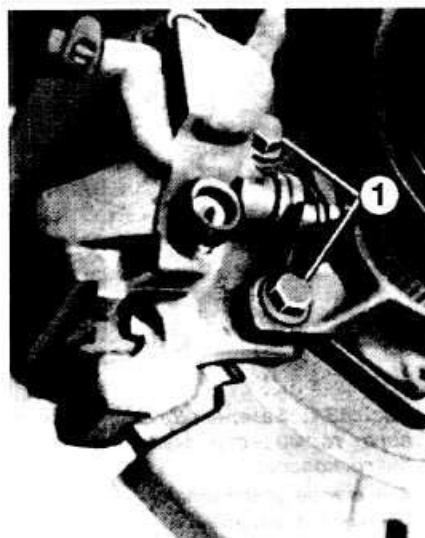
Болты 1 крепления направляющей колодок дискового тормозного механизма задних колес
